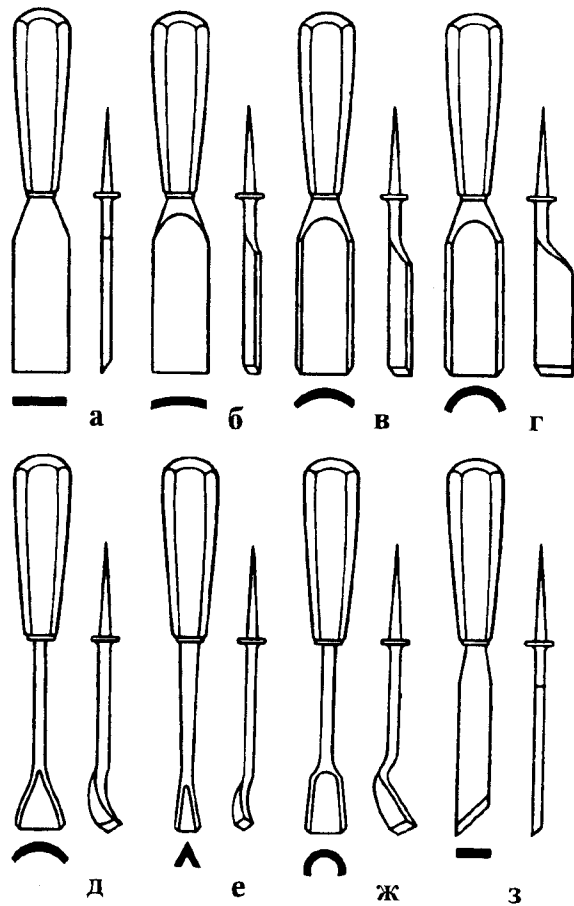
Стамески для резьбы по деревине: а — плоская прямая; б, в, г — желобчатые: б — средняя, в — кругая, г — полукруглая; д — клюкарза; е — уголок; ж — церазик; з — плоская косая (косячок)
